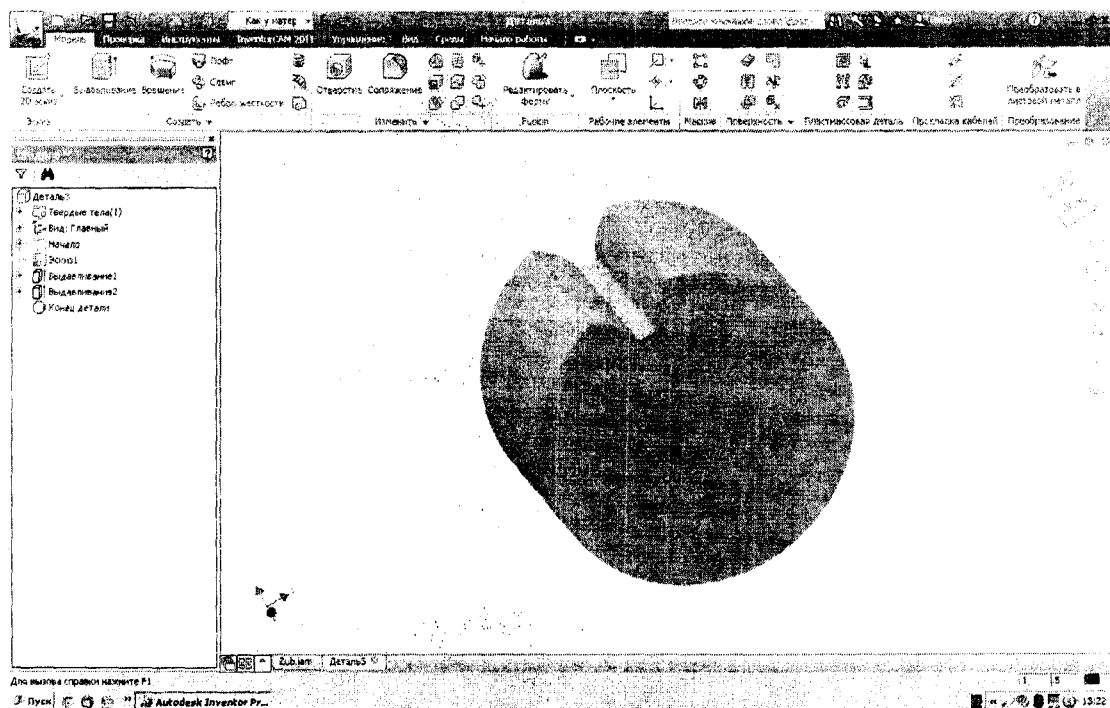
Твердотельная параметрическая модель заготовки для мелко модульного твердосплавного долбяка
